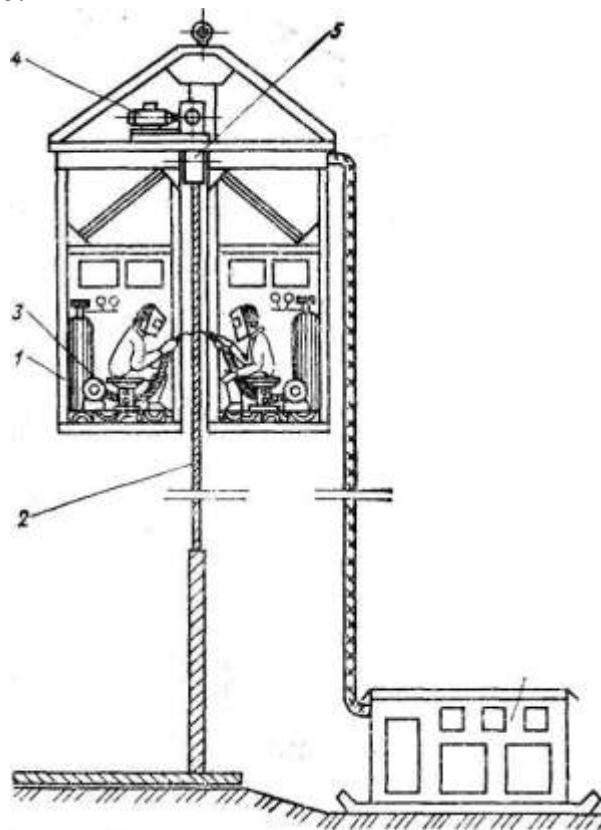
Передвижные кабины для сварки горизонтальных швов цилиндрических резервуаров
